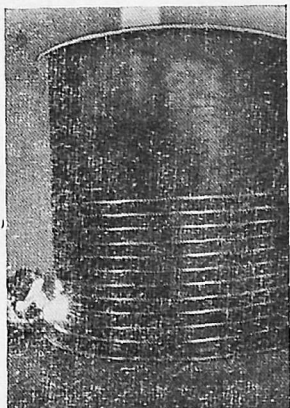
Наварка змеевика на цилиндрический корпус.
